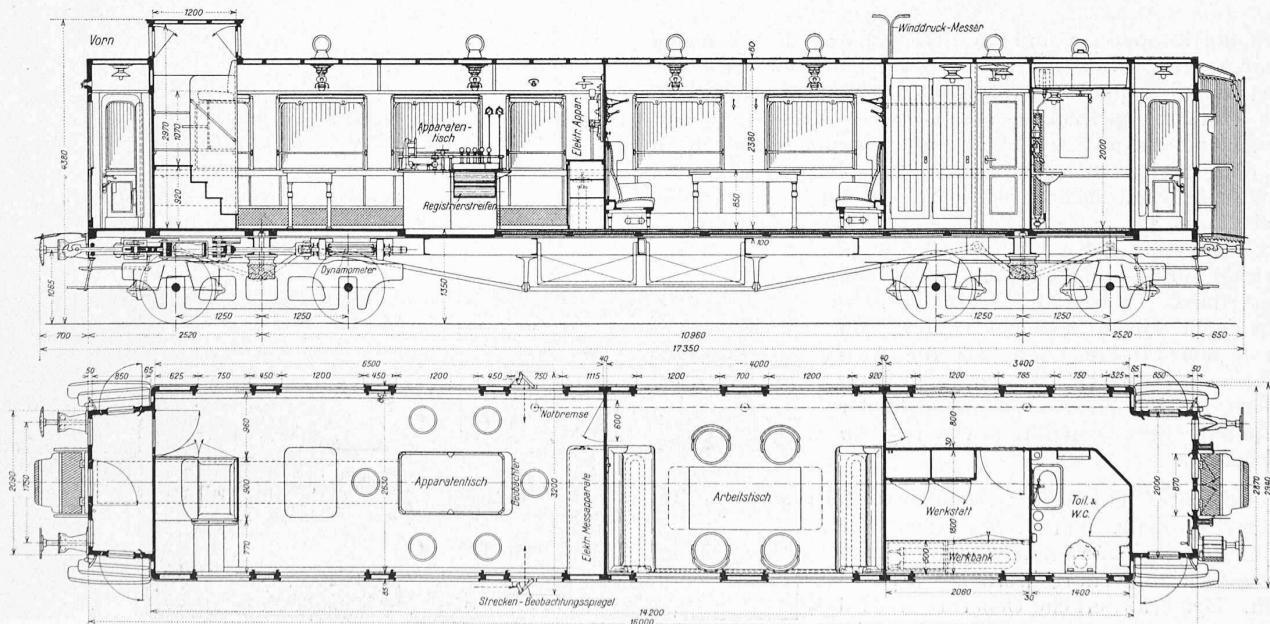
und 3. Längsschnitt und Horizontalschnitt des Dynamometerwagens. — Maßstab 1:100.
